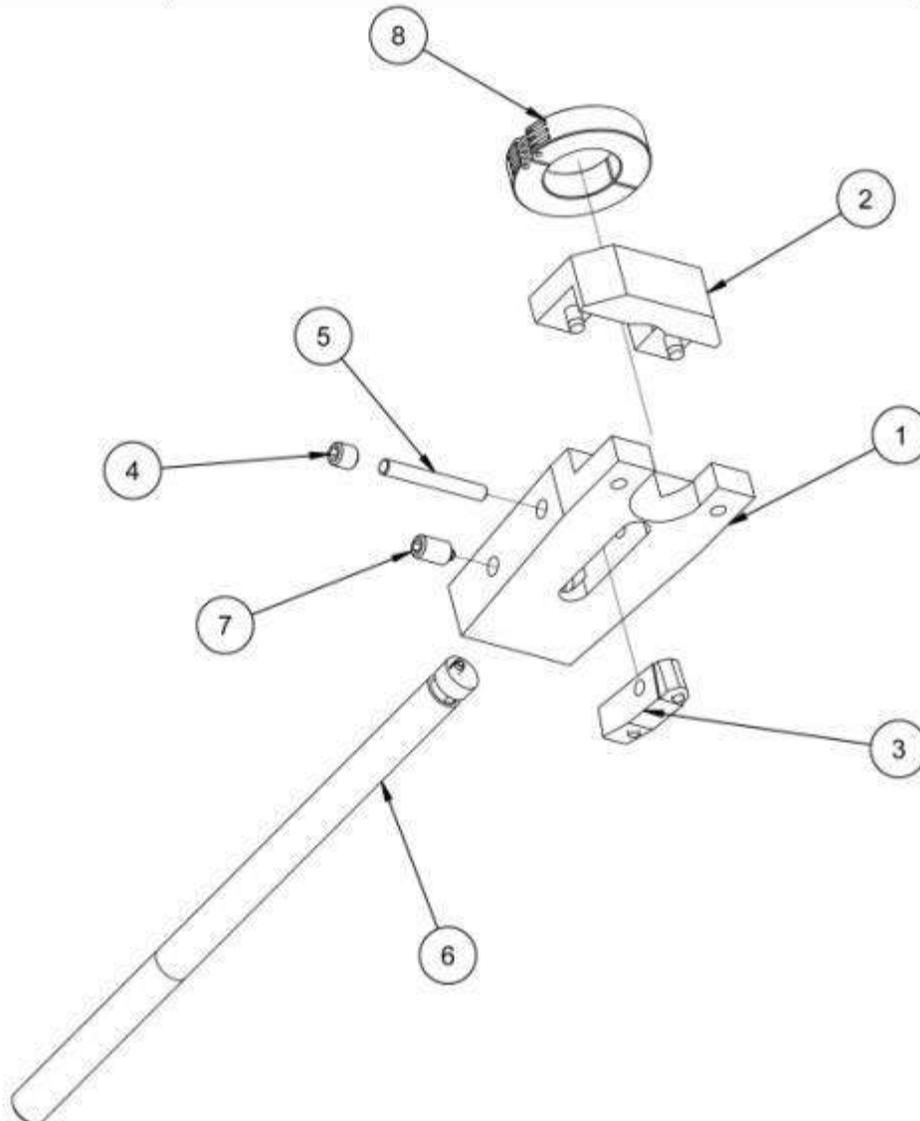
P/N ENSEMBLE D'ENTRAÎNEMENT 120 V
